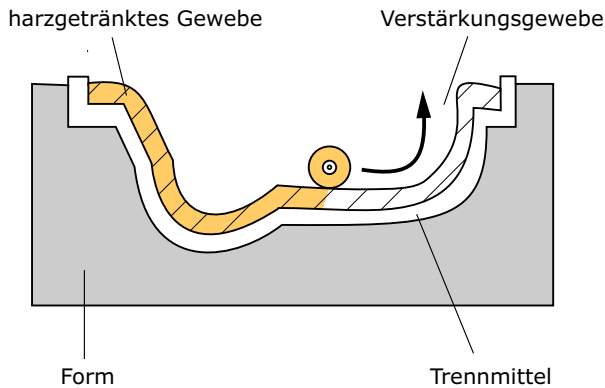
rfZ) Beim Handlaminieren wird das Gewebe von Hand mit Pinsel oder Roller getränkt
